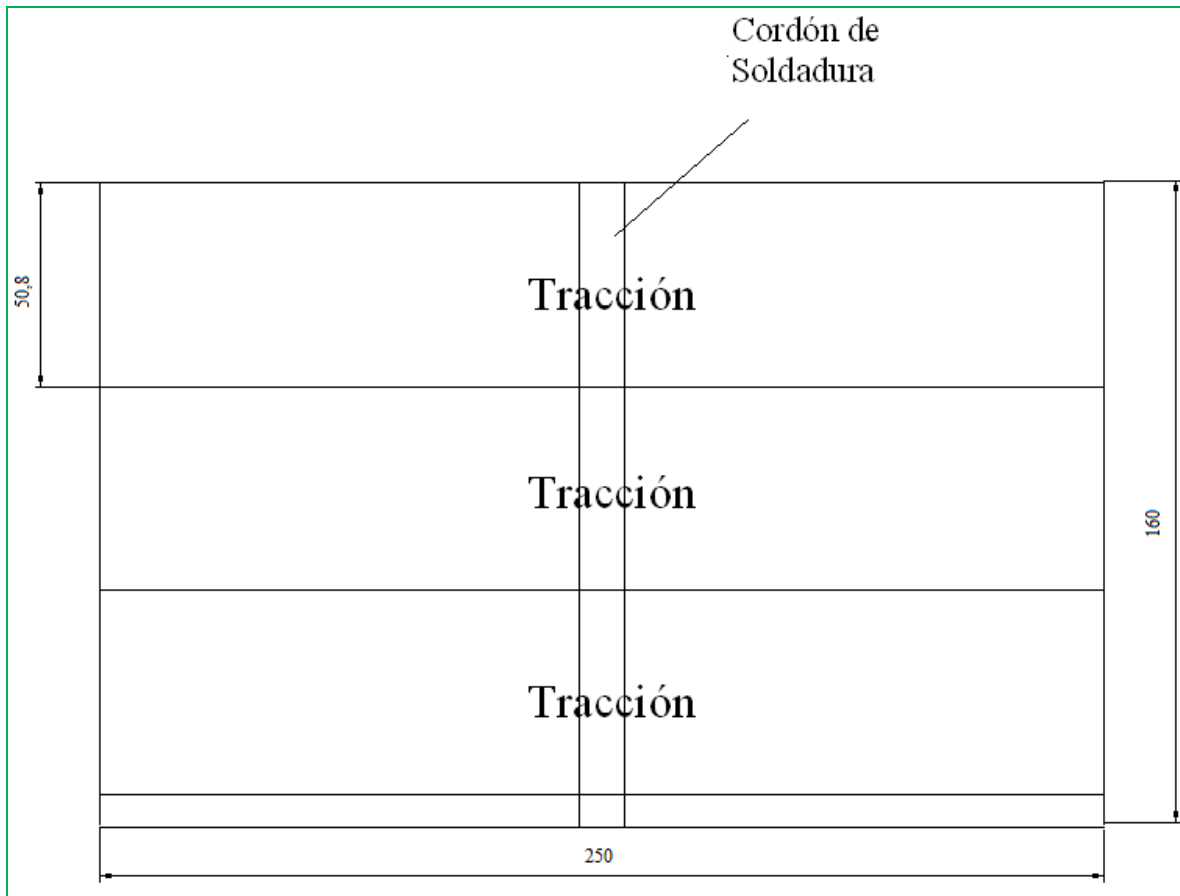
Esquema de la distribución del material soldado, láminas de 160x250, dimensiones en mm.
